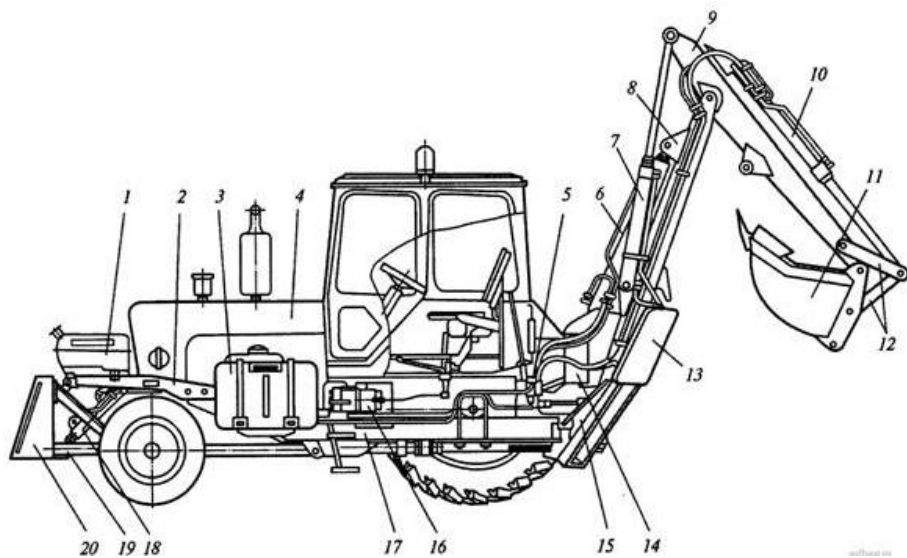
Неполноповоротный экскаватор ЭО-2621ВЗ:
